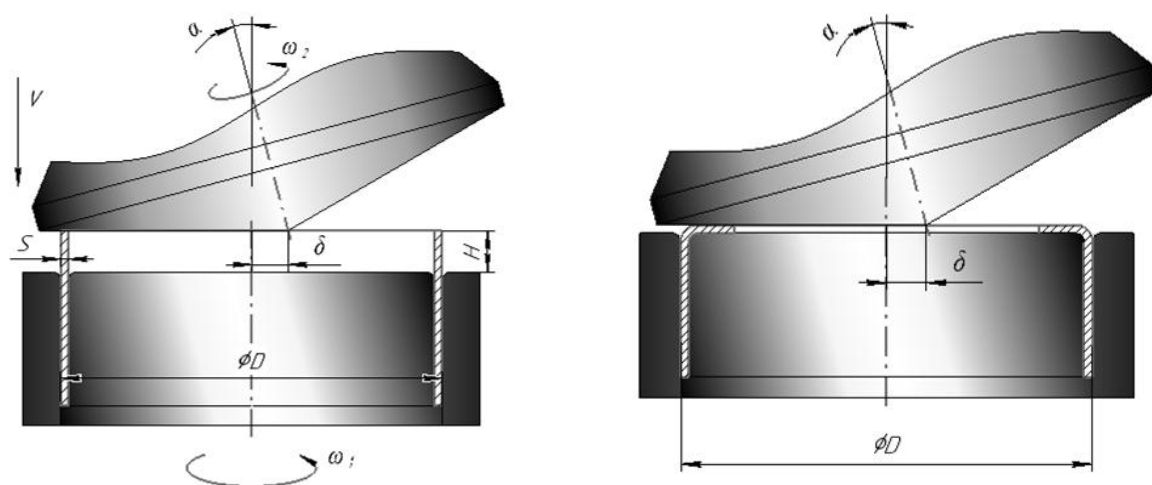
Схема торцевой раскатки трубной заготовки при формировании внутреннего фланца
